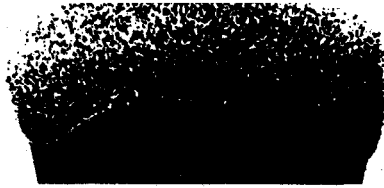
Структура кольца, полученного из низкой заготовки методом раскатки с низким очагом деформации, сплав ХН68ВМТЮК-ВД. Зерно однородное мелкое, х1.
